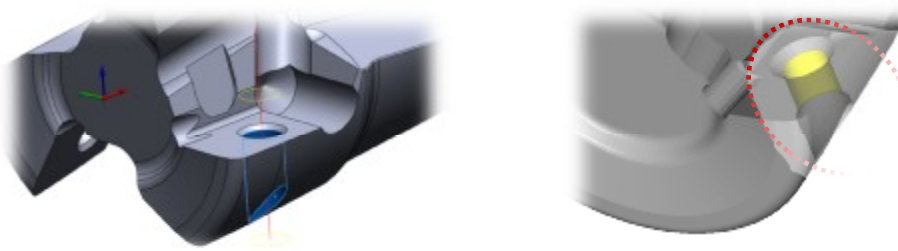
Operace 16 – vygenerované dráhy a obrobení
